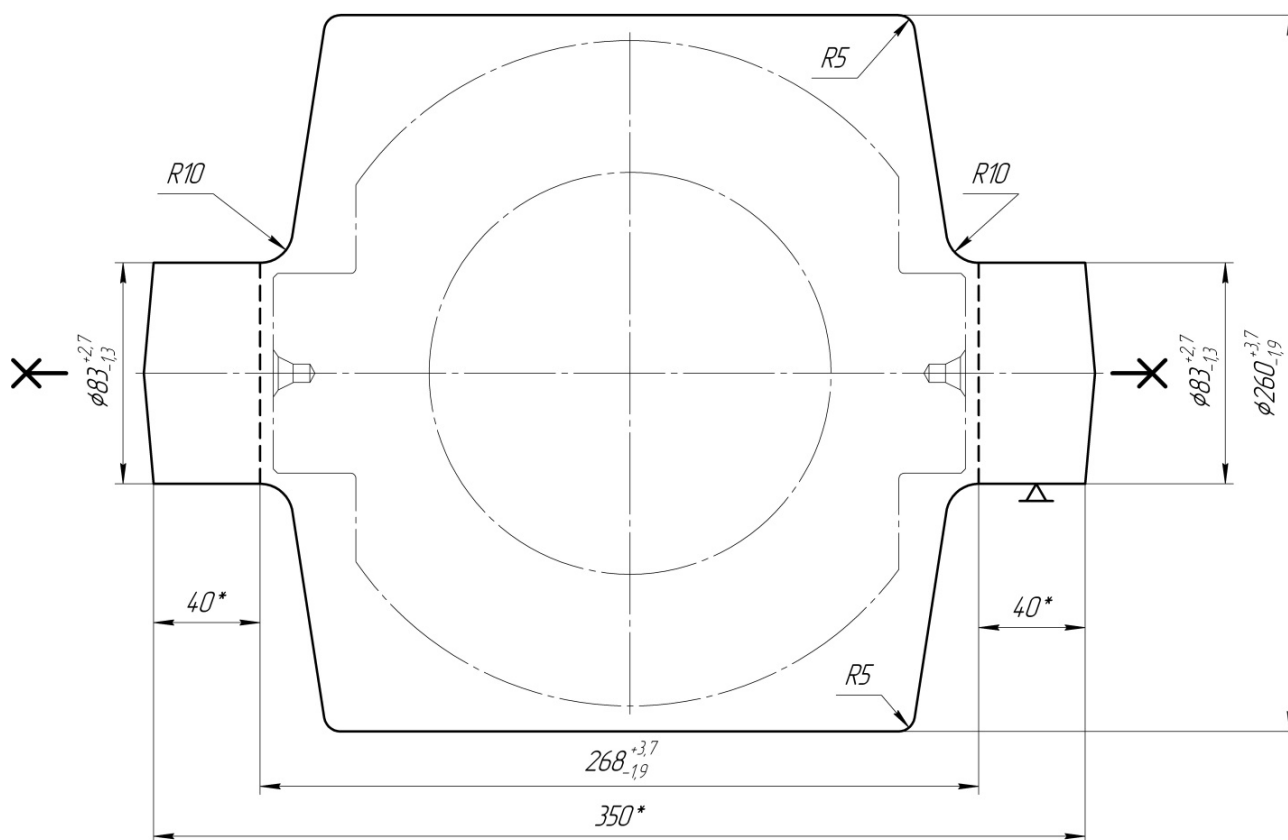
Ескіз заготовки виготовленої на молотах
